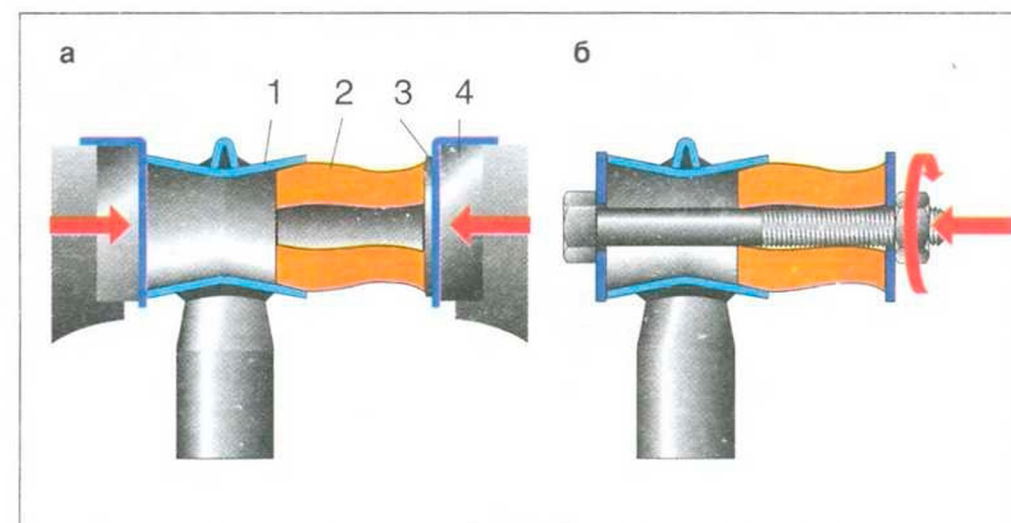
Установка в проушину резиновой втулки: а – в тисках; б – с помощью болта; 1 – проушина; 2 – втулка; 3 – шайба; 4 – тиски
